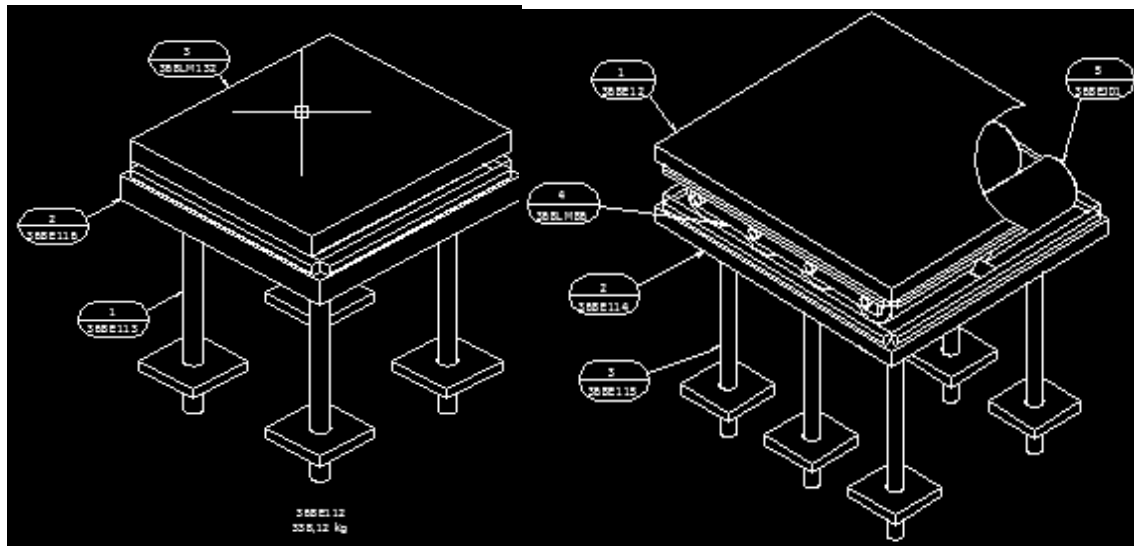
PLANO DE MONTAJE APOYO FIJO MÓVIL, SUMINISTRADO POR LA EMPRESA SERVIMECOL.
